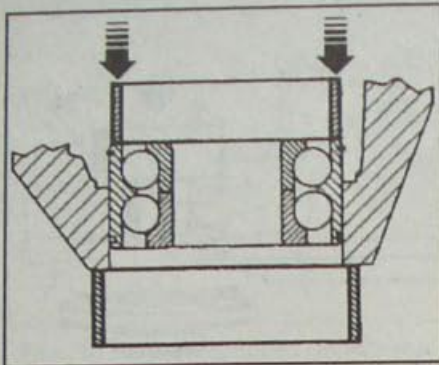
Использование прессы и оправок Rou. 1392 и Т. Ав. 1230 для запрессовки наружного кольца подшипника в поворотный кулак
